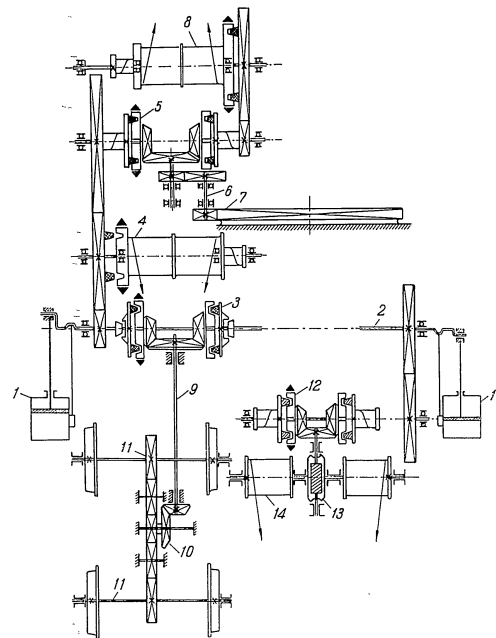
Кинематическая схема парового крана ПК-25: 1 - паровая машина; 2 - кривошипный вал; 3 - реверс механизма передвижения; 4 - главная лебедка; 5 - реверс поворотного механизма; 6 - вертикальный вал поворотного механизма; 7 - зубчатый венец; 8 - грейферный барабан; 9 - центральный вертикальный вал; 10 - шестеренные передачи механизма передвижения; 11 - ведомая шестерня на приводной оси тележки; 12 - реверс стрелоподъемной лебедки; 13 - червячная передача; 14 - барабан стрелоподъемной лебедки
